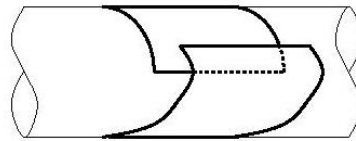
Enrouler le papier pour le calibrage
